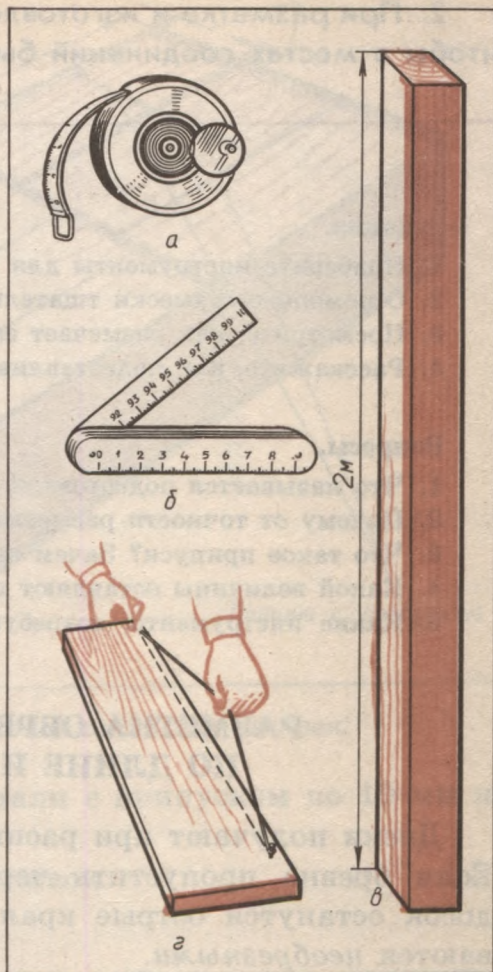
Инструменты для подготовки пиломатериалов к раскрою: а — рулетка; б — складной метр; в — планка; г — шнурок.
